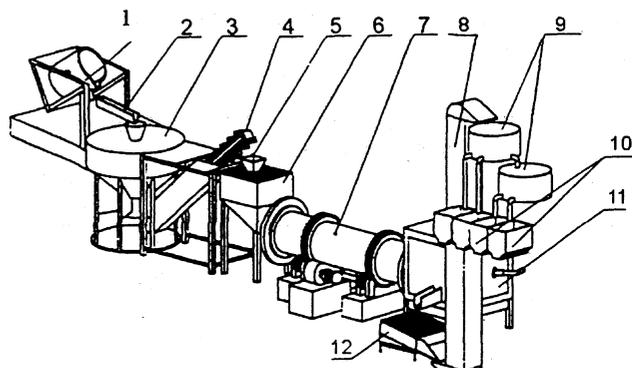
Схема комплекса оборудования для литья дробы мод. 46145: 1 – ковш; 2 – желоб металлоприемника; 3 – дробелитейная машина; 4 – наклонный элеватор; 5 – приемная воронка; 6 – бункер печи; 7 – барабанная печь; 8 – элеватор; 9 – вибростата; 10 – тара для сбора дробы по фракциям; 11 – блок горелочной печи; 12 – агрегат рассева дробы
